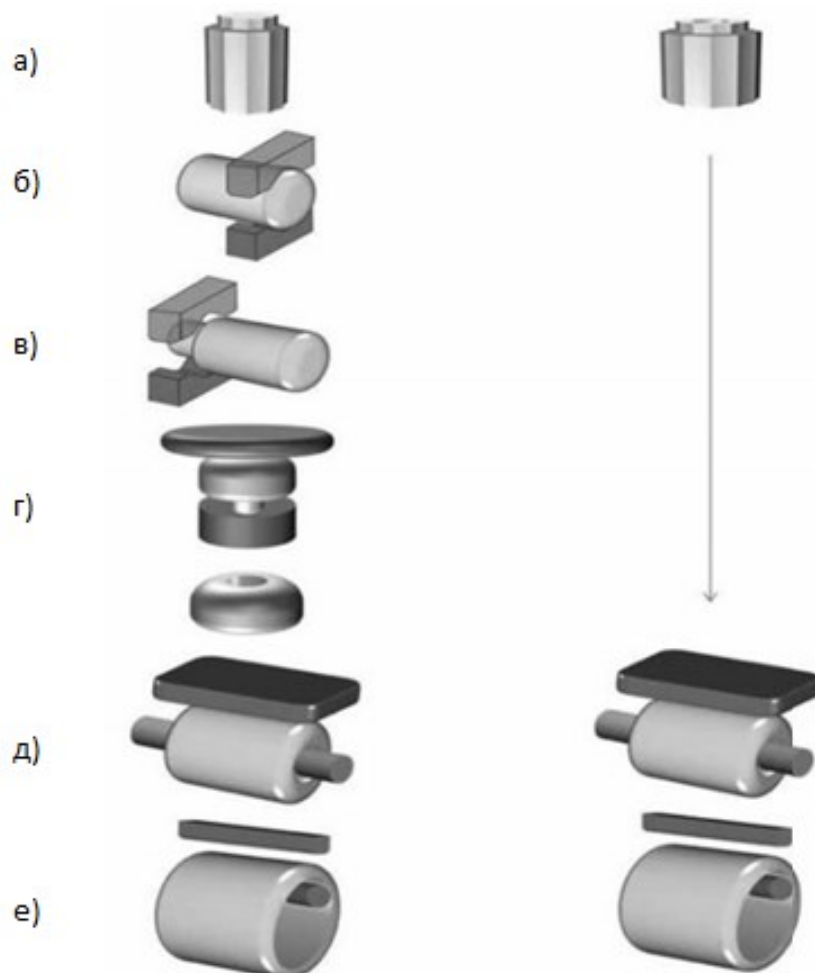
Схема виробництва кованих порожнистих заготовок:
